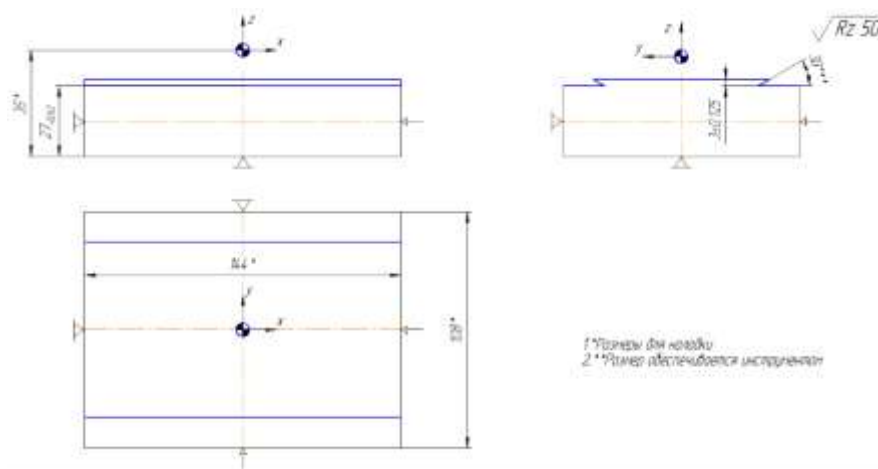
Обрабатываемая поверхность
